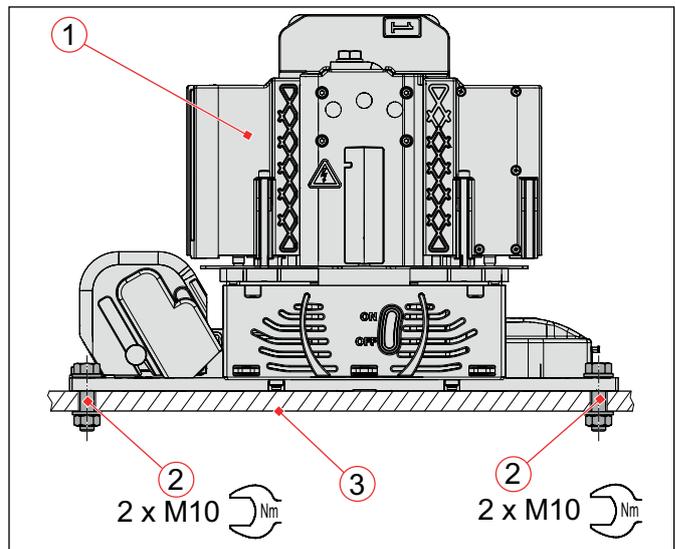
CA 1115/CA 1130: Beispiel für Montage des Schützes auf Montageplatte bzw. Einbaurahmen
